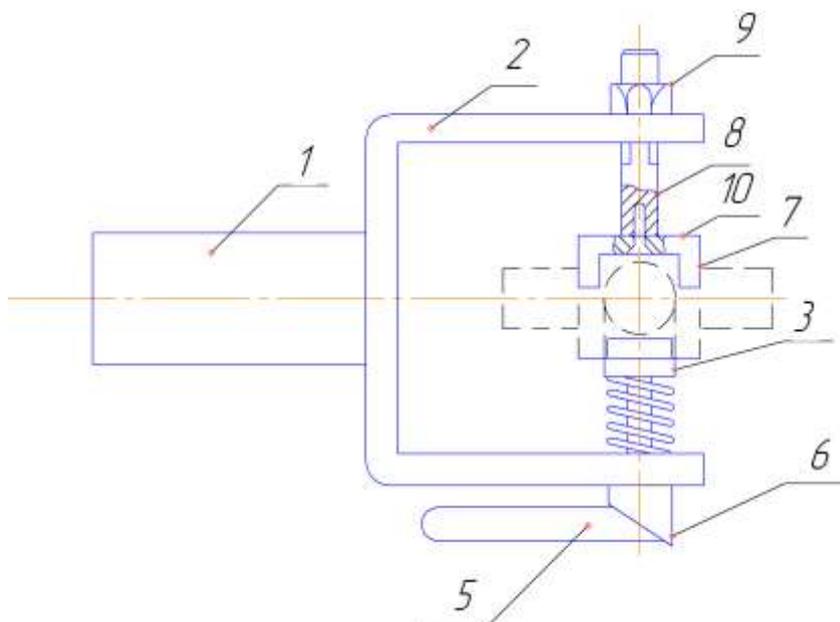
Общий вид приспособления для фиксации крестовины
